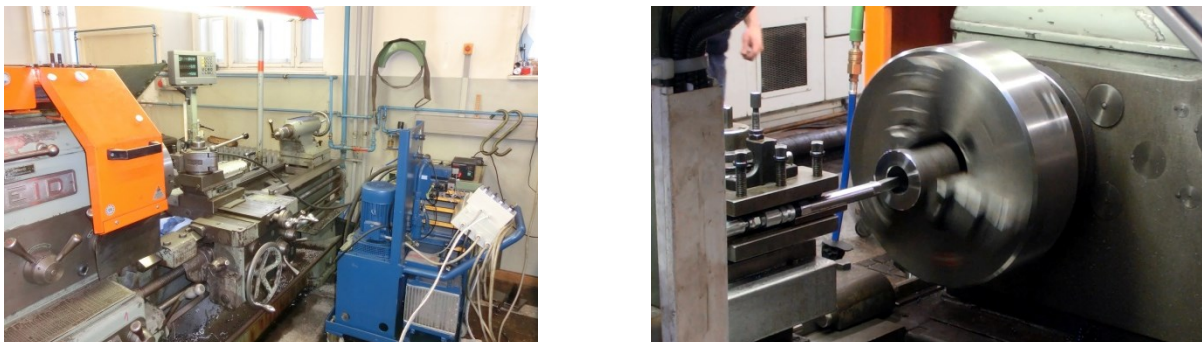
Versuchsaufbau von vorne mit Hydraulikaggregat (links) und von hinten mit eingespanntem Werkzeug im Eingriff (rechts)
